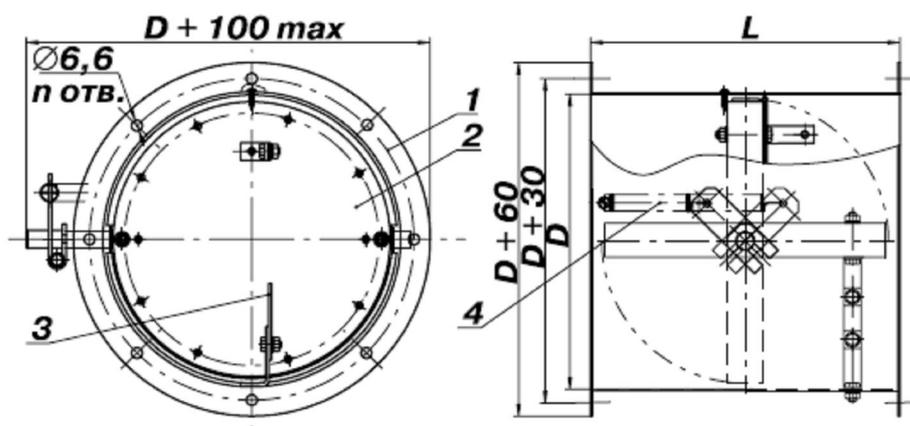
Круглый клапан с плавким предохранителем и возвратной пружиной: 1 – корпус; 2 – лопатка; 3 – плавкая вставка; 4 – пружина
